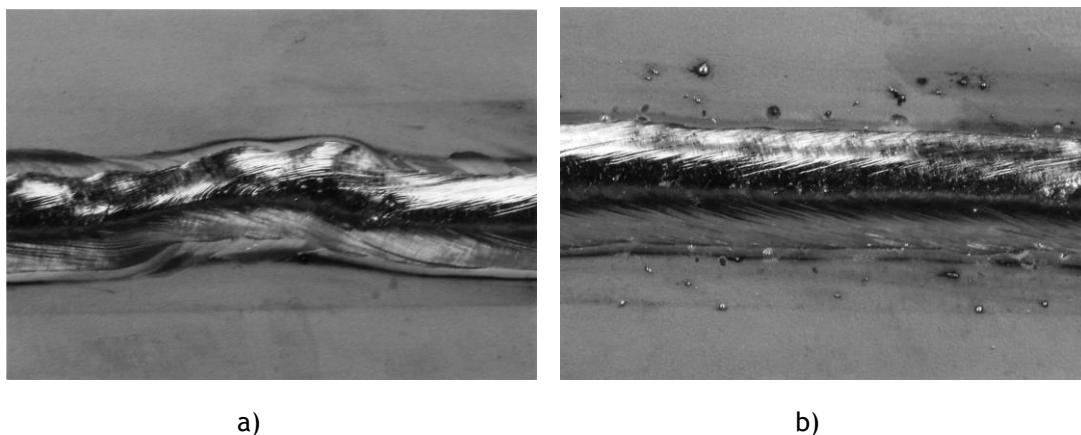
Cordões de titânio obtidos por soldadura MIG: a) efeito *wandering*; b) correção obtida pelo método da vibração
